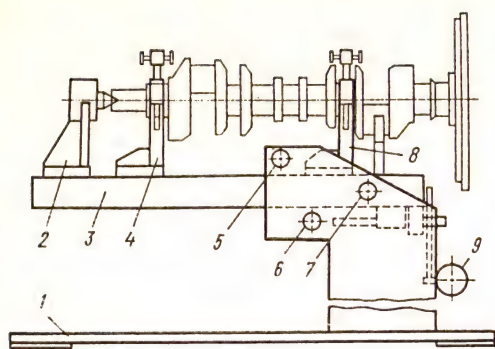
Стенд для сборки коленчатого вала с маховиком:
